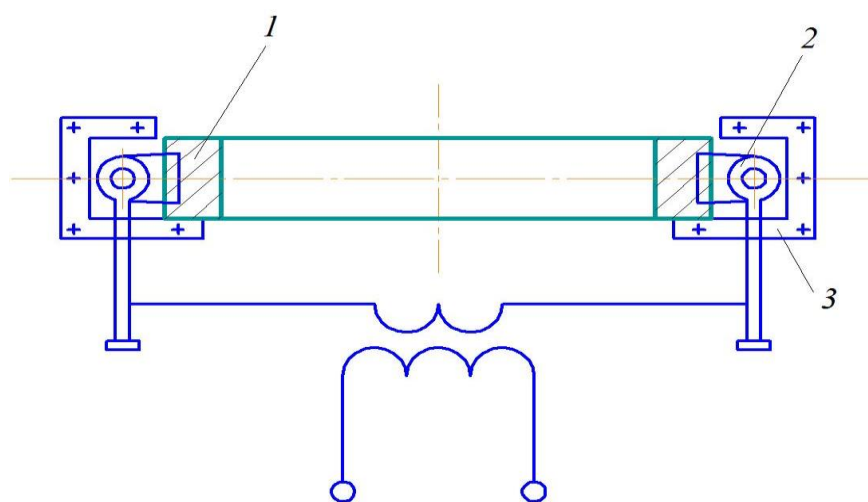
Схема индукционного нагревателя с индукторами, охватывающими деталь:
